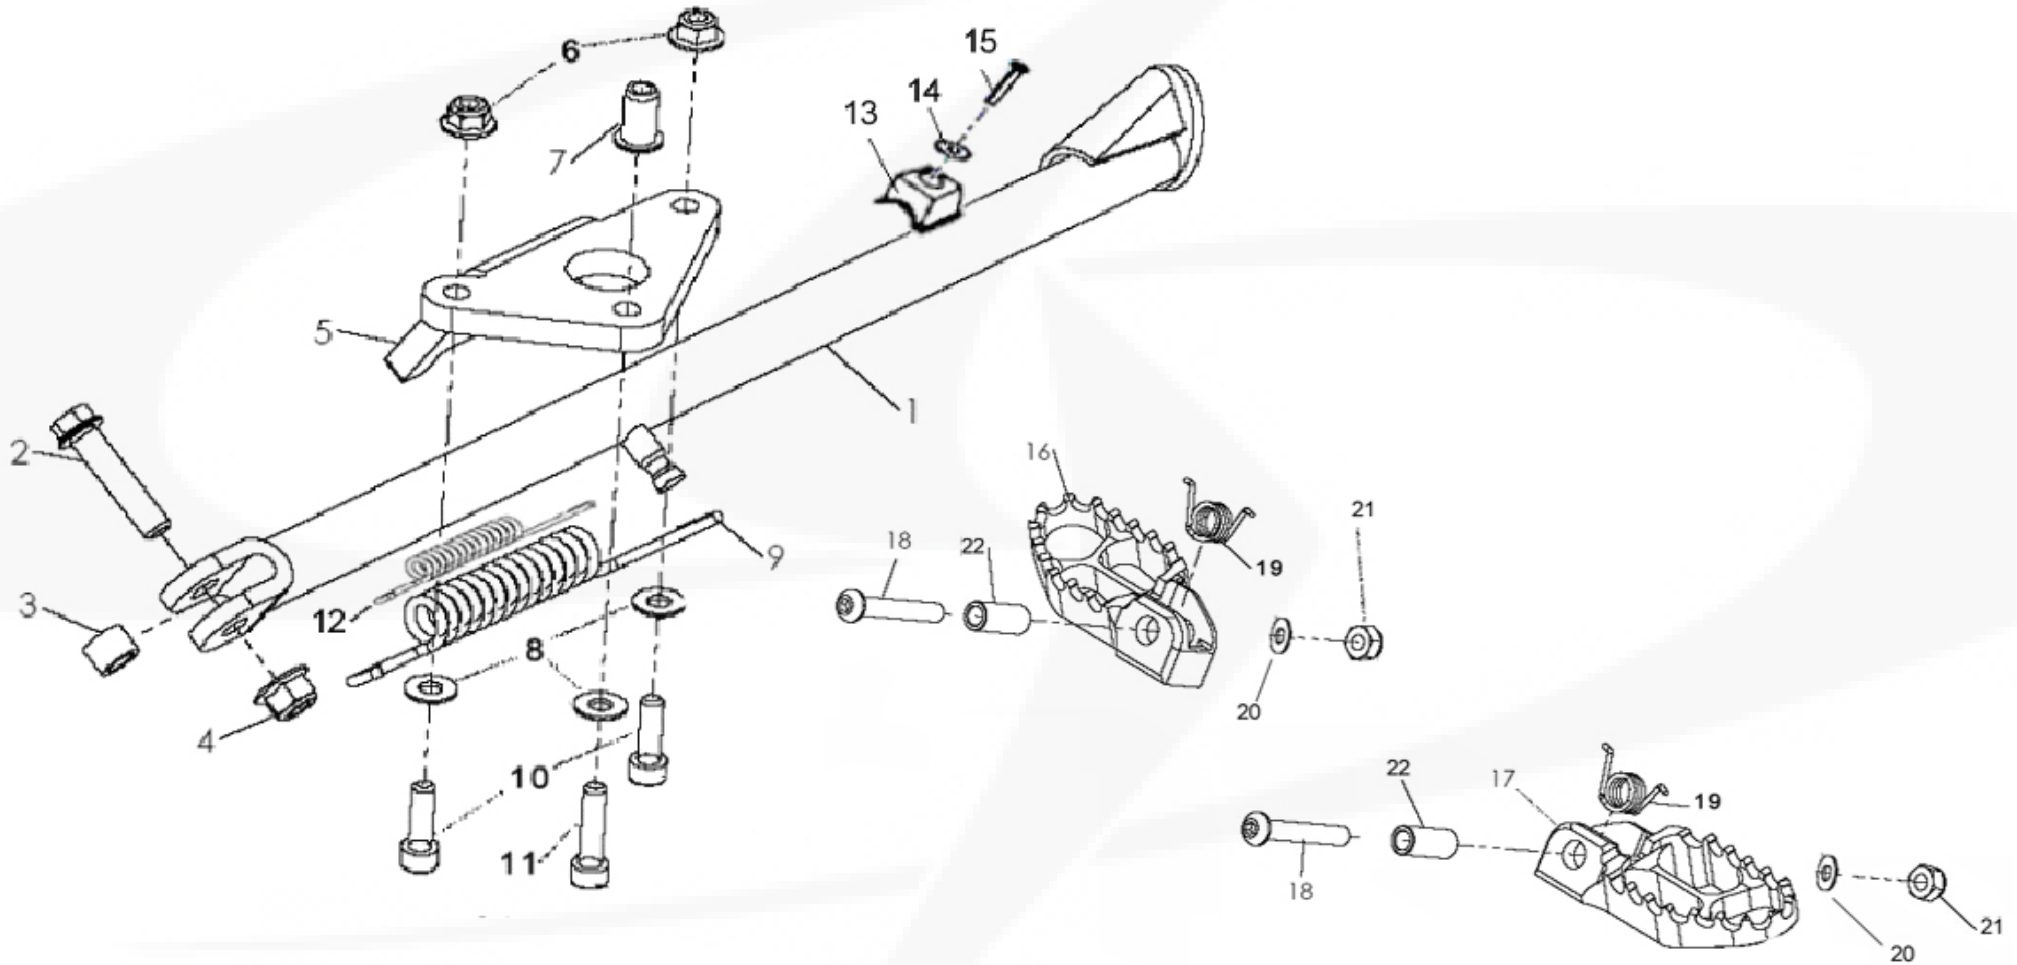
BÉQUILLE ET REPOSE-PIEDS / STAND AND FOOTREST / CABALLETE Y ESTRIBOS
